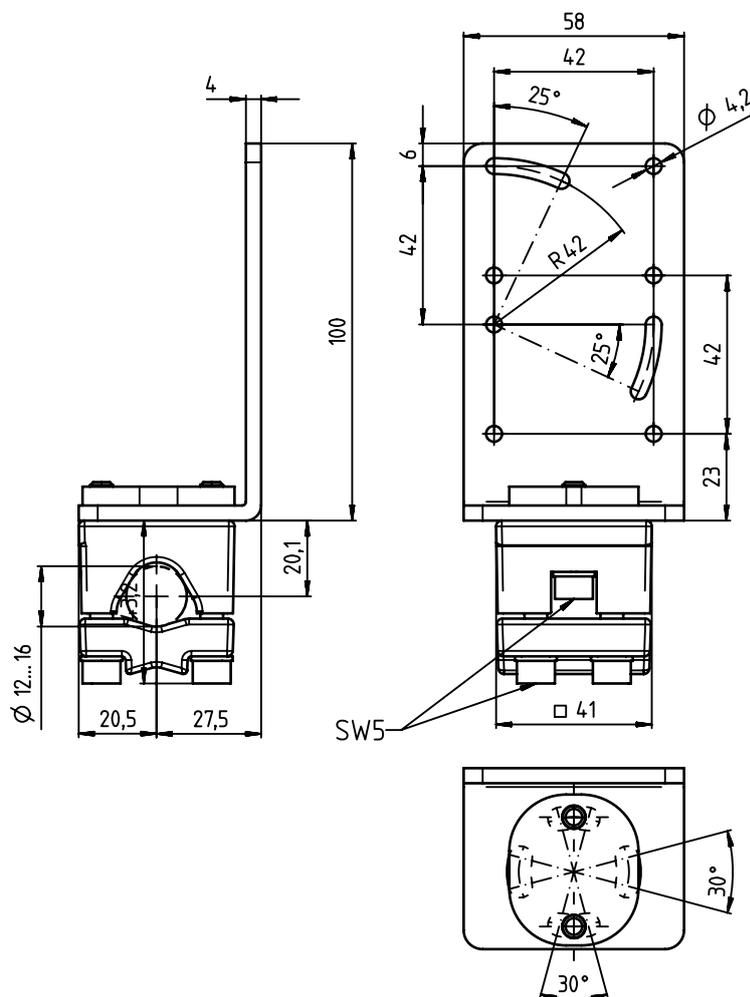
Disegno quotato staffa di fissaggio BT 300-W
